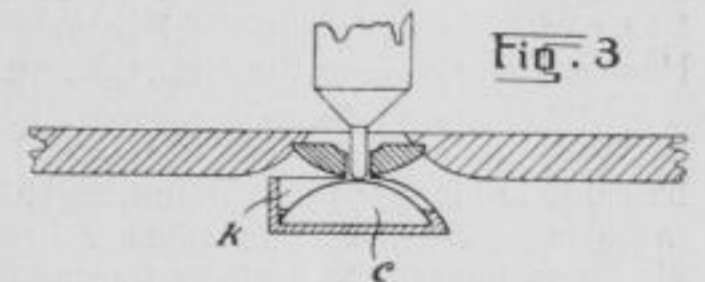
zeigt eine Ansicht des Stellzeigers, Figur 2 ist ein Schnitt durch das Lager nebst Deckstein, Figur 3 eine abweichende Ausführung.
